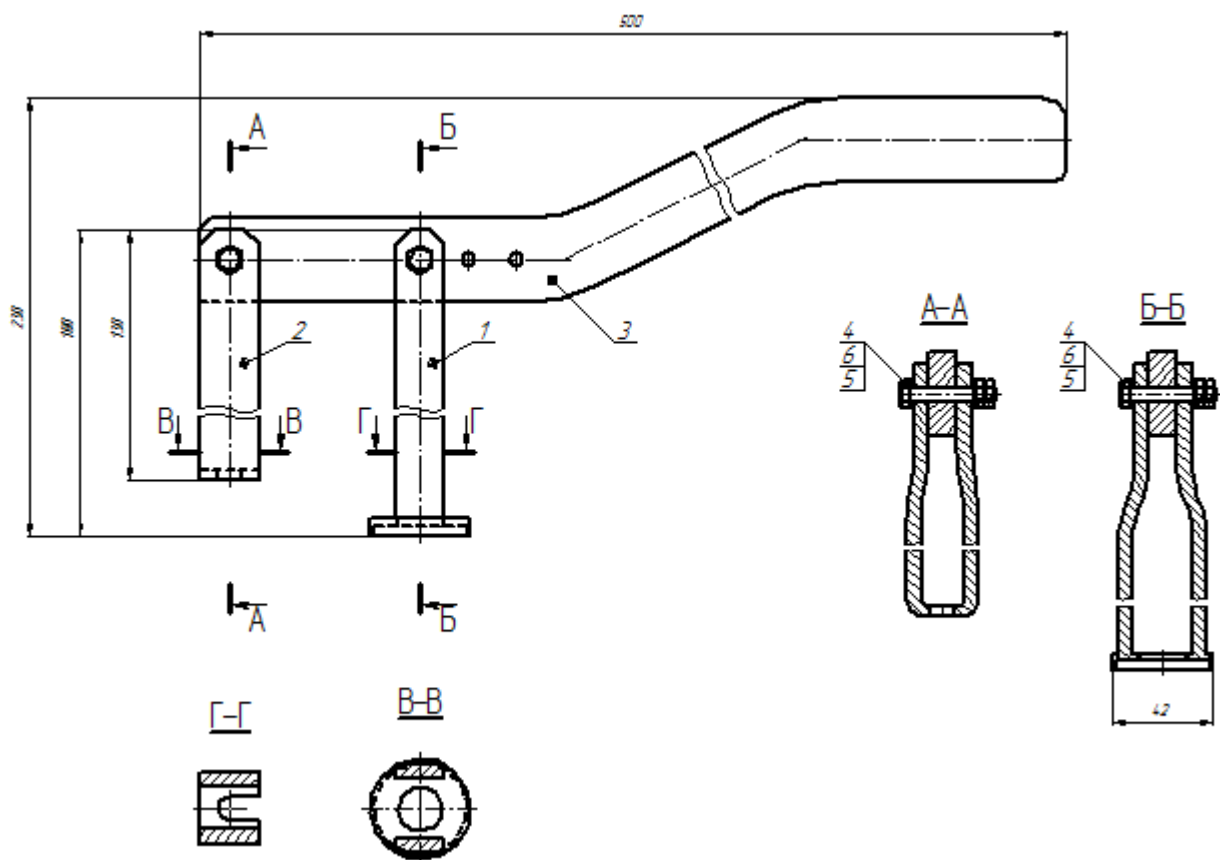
Пристрій для розсухарювання клапанів
